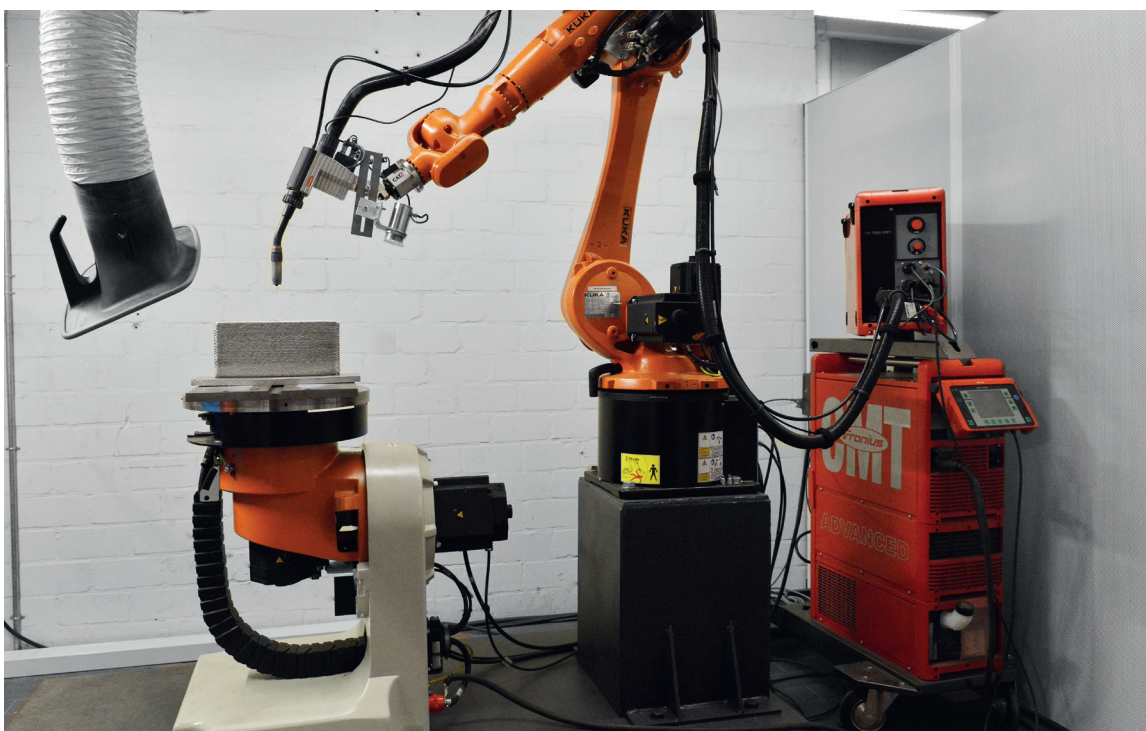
WAAM am Institut für Füge- und Schweißtechnik
